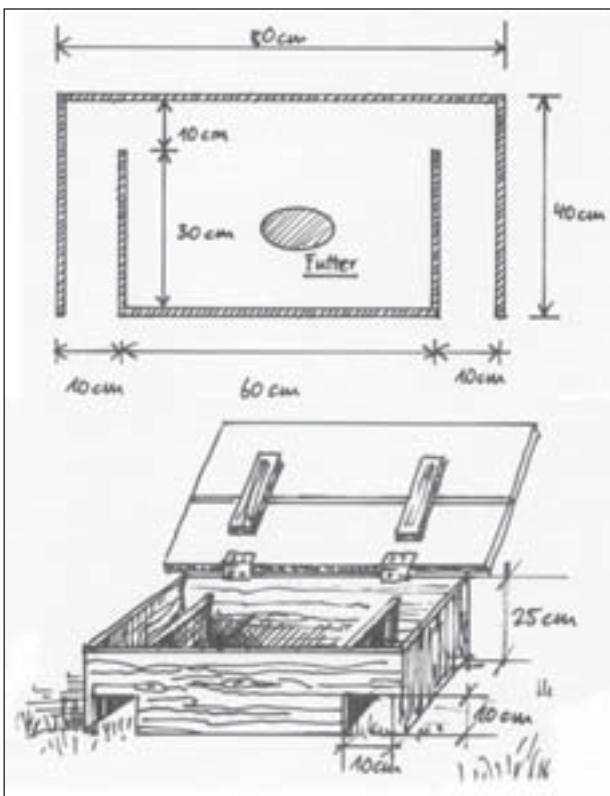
Grundriss (oben) und Ansicht eines ziemlich katzensicheren Futterhauses.
